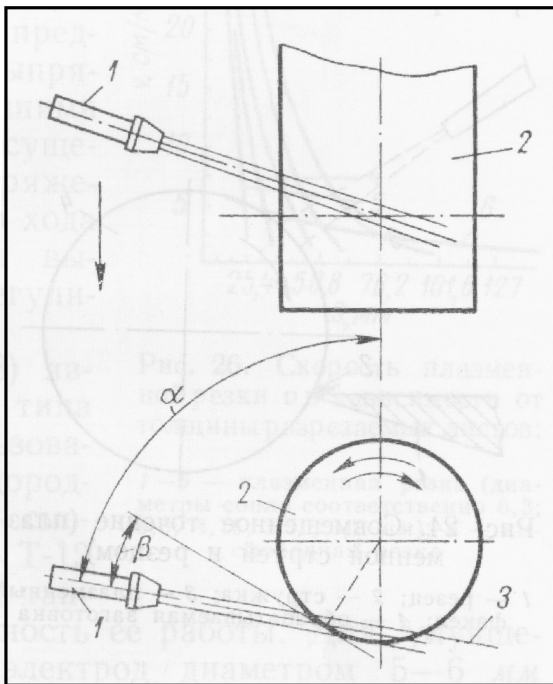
Схема точіння плазмовим струменем: α - кут нахилу горілки до вертикалі; β - кут різання; 1 - плазмова горілка; 2 - деталь; 3 - вісь струменю
